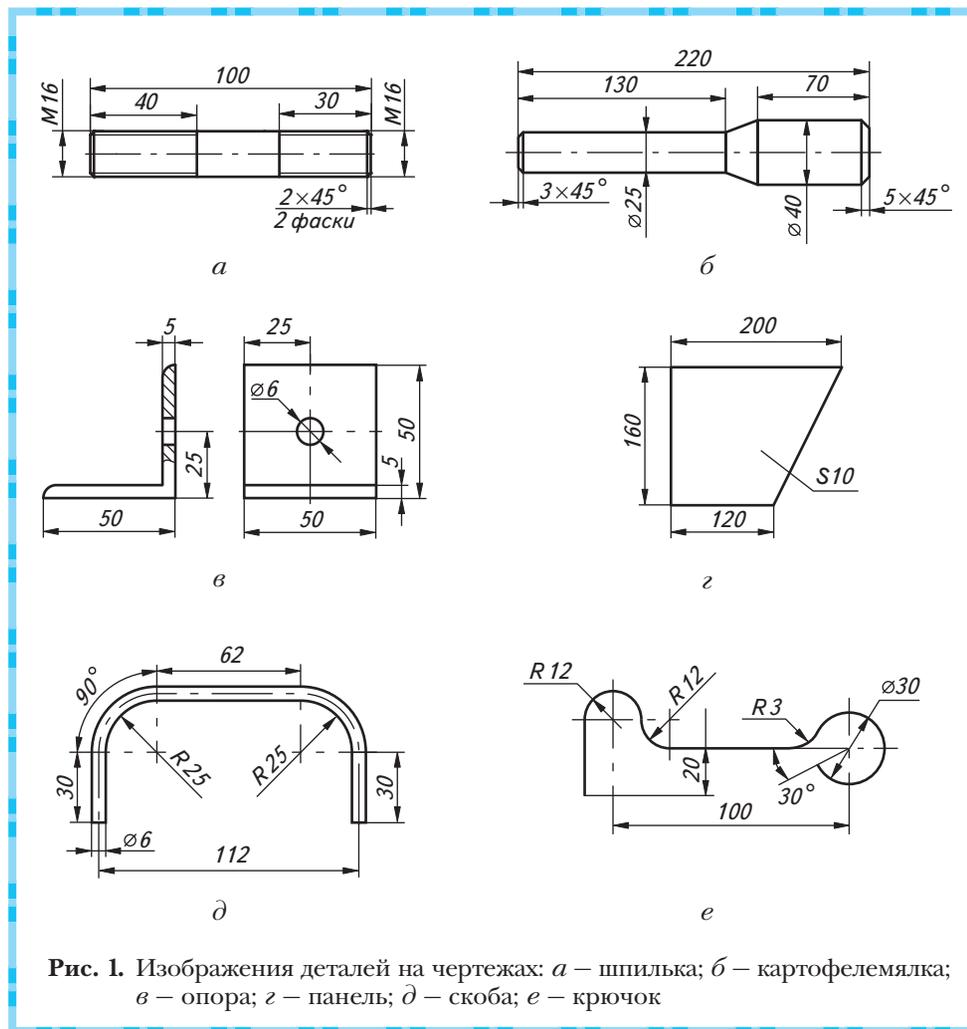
Изображения деталей на чертежах: а – шпилька; б – картофелемялка; в – опора; г – панель; д – скоба; е – крючок
